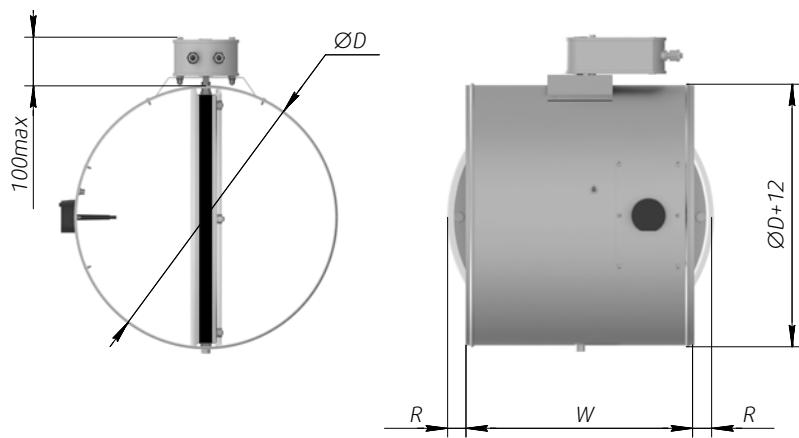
б. Размеры ниппельного клапана HELMER, EI60
